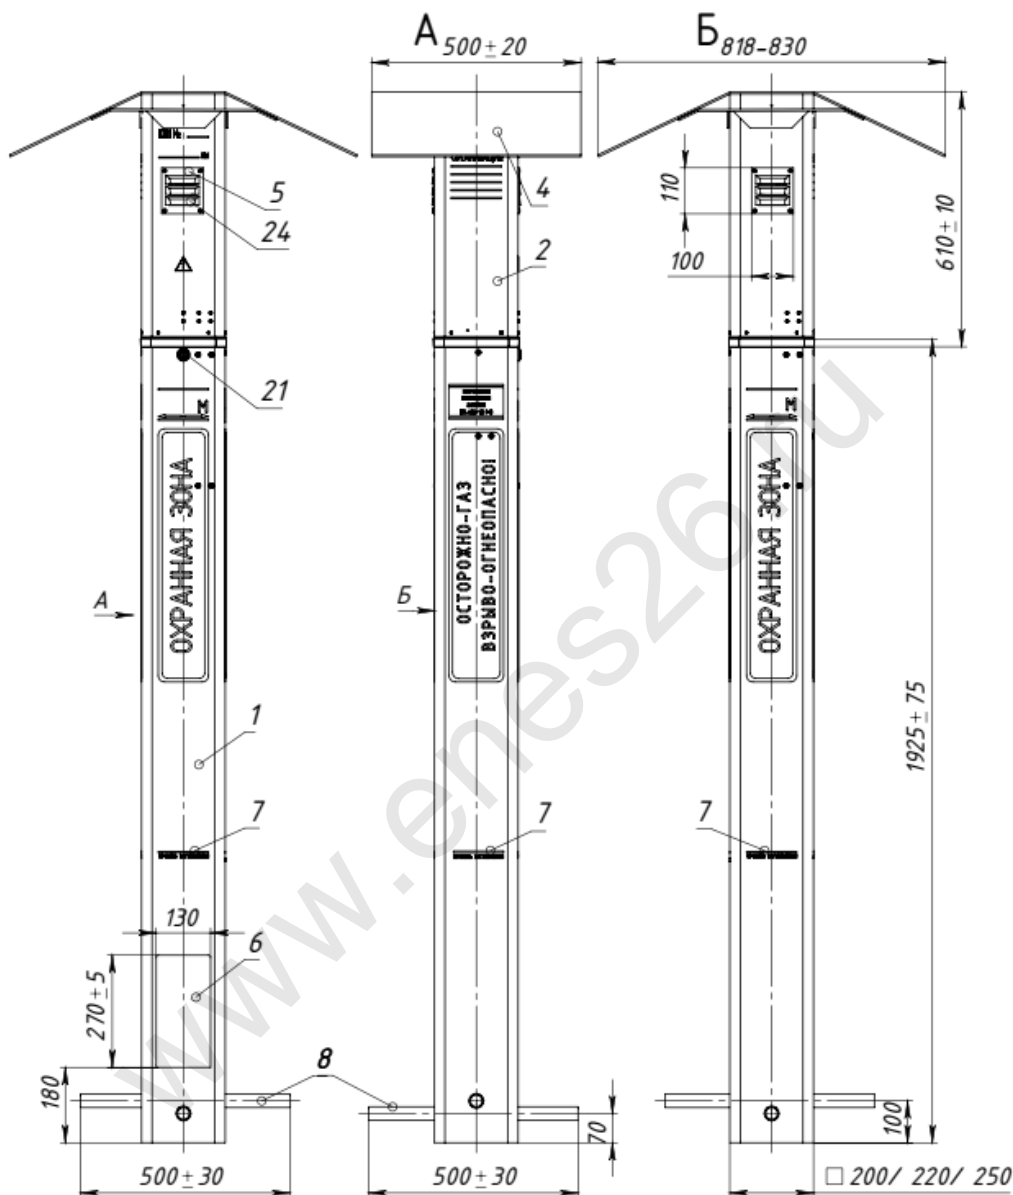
Корпус ЗГАНС® УКМ-КИП с километровым знаком
